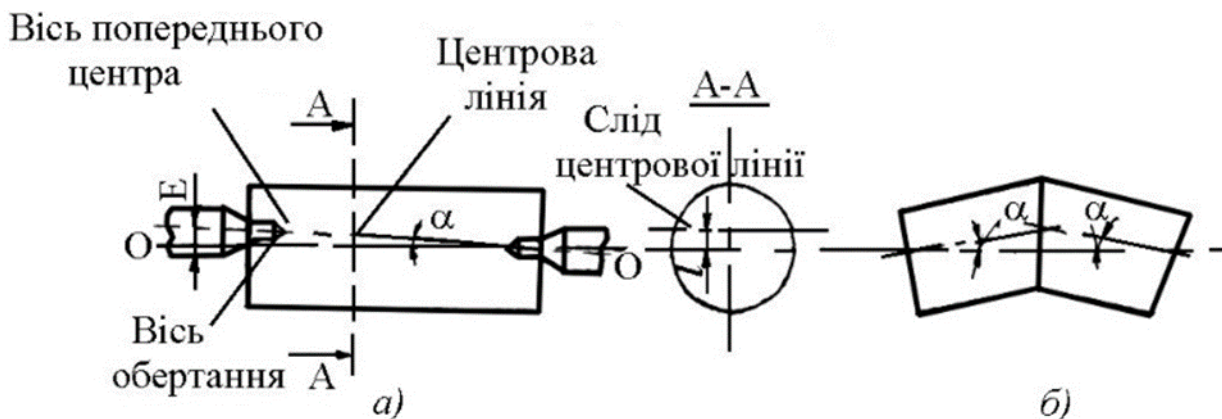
Вплив биття переднього центра на точність обробки: а – похибка при обточуванні за одне встановлення; б – похибка при обточуванні з переустановленням заготовки
